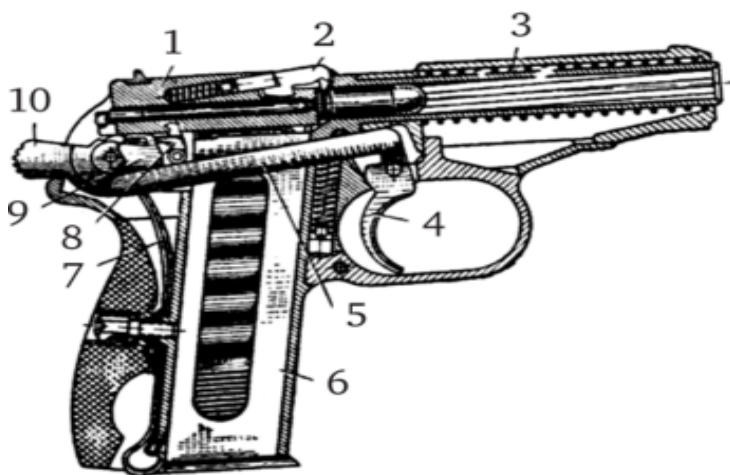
Положение частей и механизмов пистолета перед выстрелом; 1 – затвор; 2 – выбрасыватель; 3 – возвратная пружина; 4 – спусковой крючок; 5 – спусковая тяга; 6 – магазин; 7 – боевая пружина; 8 – шпатель с пружиной; 9 – рычаг взвода; 10 – курок
